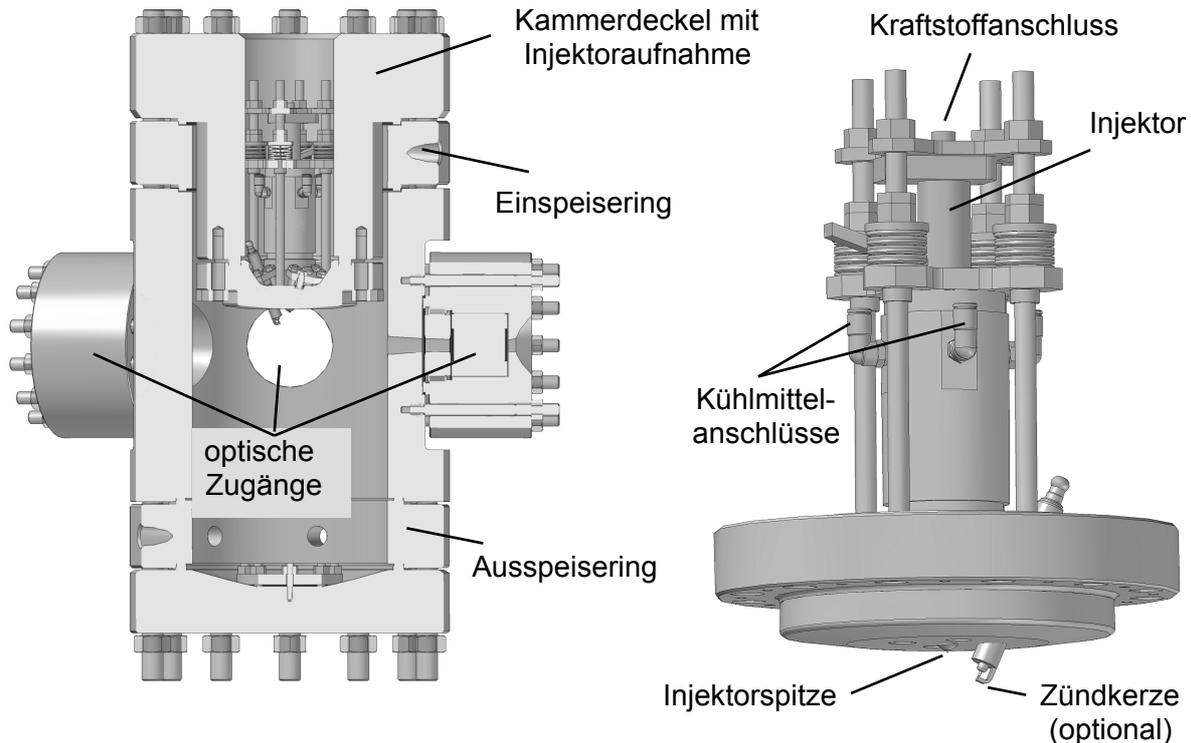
Schnitt durch die Druckkammer (links) sowie Injektoraufnahme (rechts)
